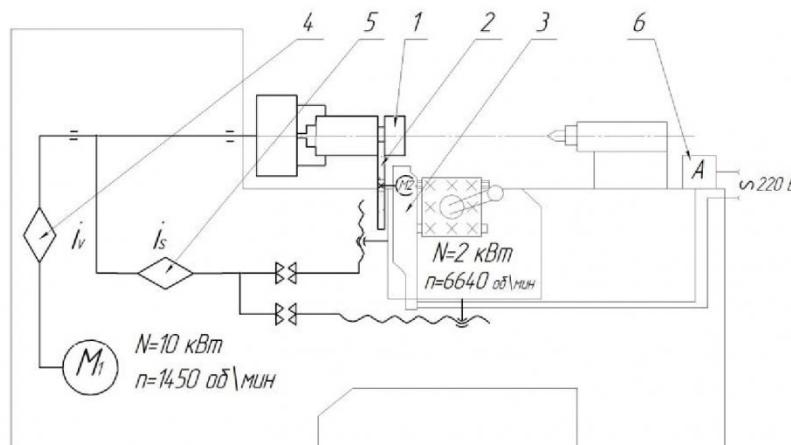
Испытательный стенд на базе токарного станка с закреплённой УШМ для испытания отрезных кругов по схеме круглого шлифования
